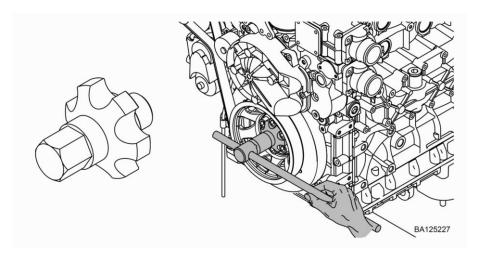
Dispositivo de giro - Montaje de la polea de transmisión del cigüeñal, herramienta especial núm. 30c
